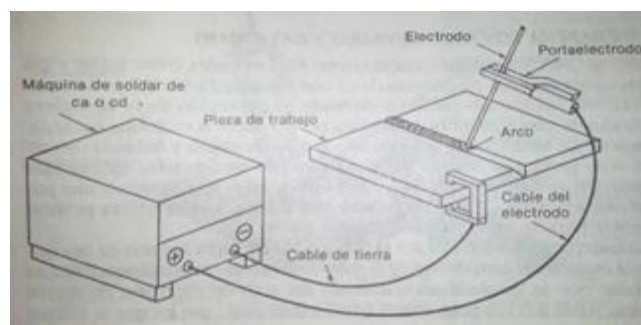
Equipo para realizar soldadura eléctrica.
